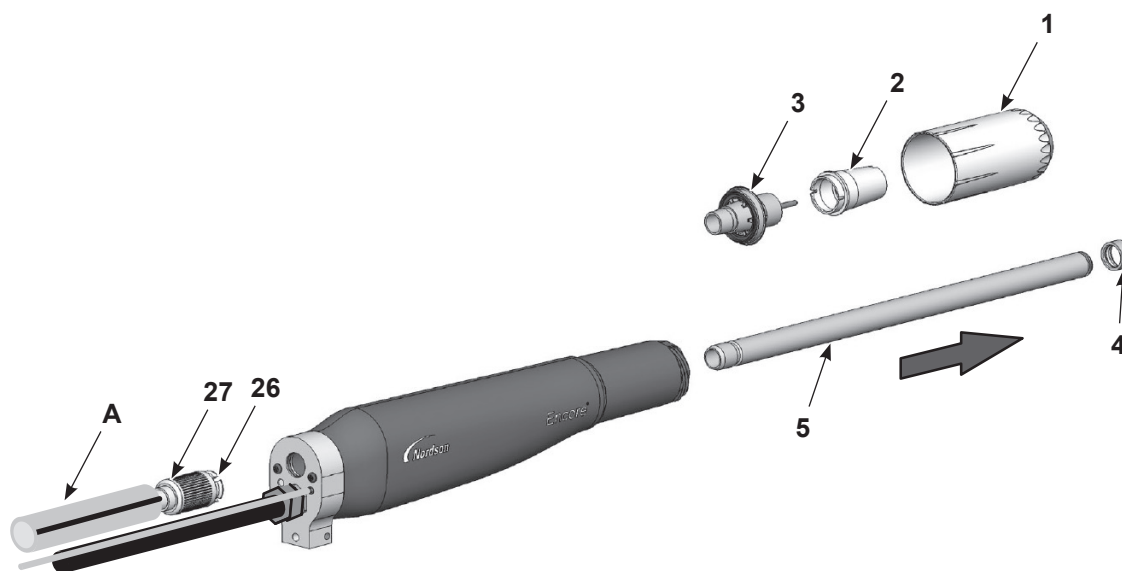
Техобслуживание – распылитель, монтируемый на штанге, показан без шарнирного крепления
